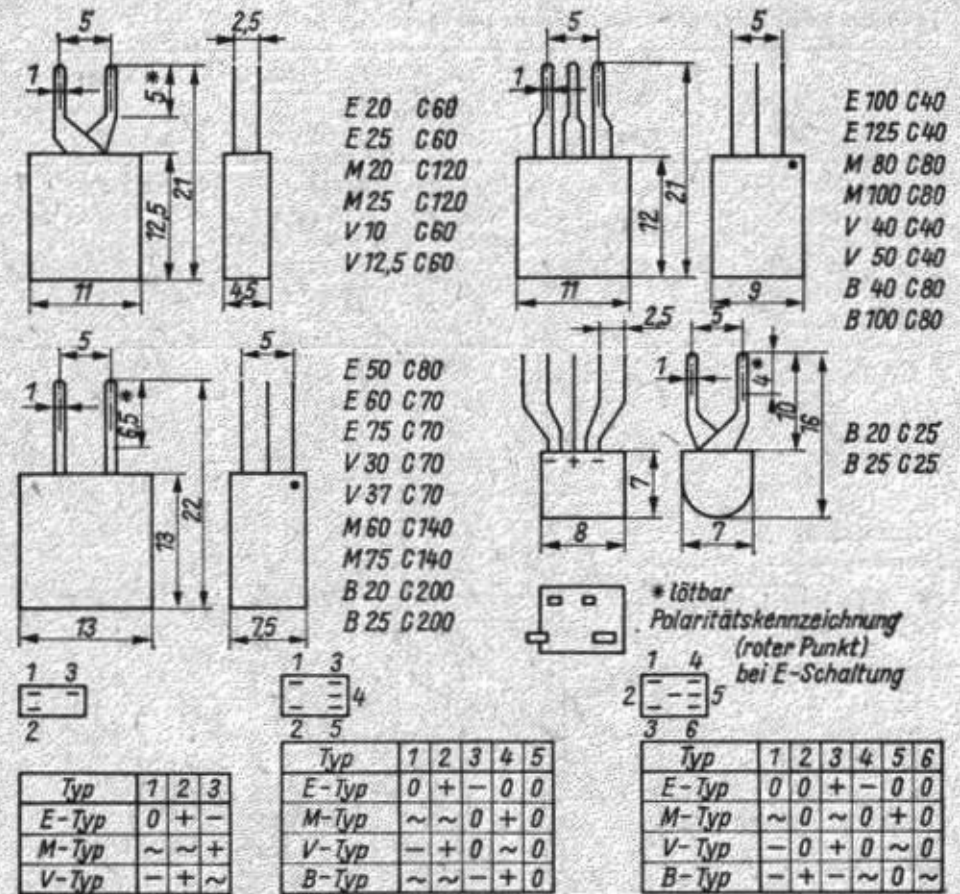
Bauformen der Selenkleinstgleichrichter für gedruckte Schaltungen
